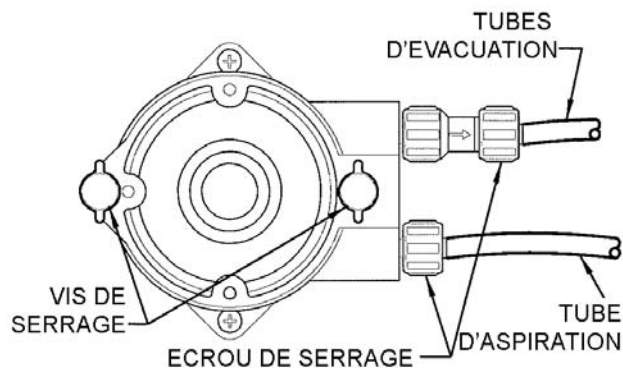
Assemblage de tête de pompe muni d'un revêtement sur l'avant de l'assemblage
